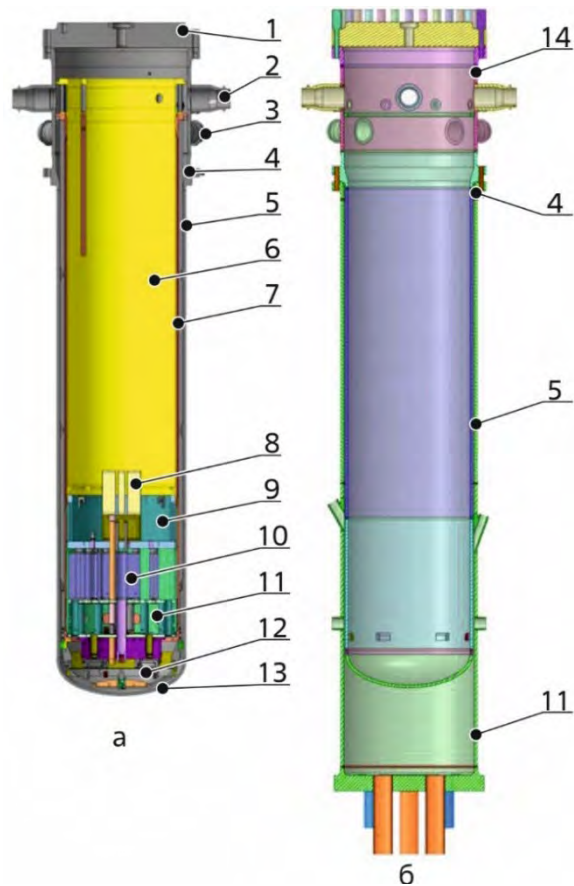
Общий вид реактора СМ (а), его корпуса и несущей конструкции (б): 1 — крышка корпуса; 2 и 3 — патрубки подвода и отвода теплоносителя соответственно; 4 — фланец соединения с несущей конструкцией; 5 — корпус; 6 — разделитель потока; 7 — экран; 8 — хранилище ТВС; 9 — прижимная решётка; 10 — блоки бериллиевого отражателя; 11 — несущие конструкции центральной зоны (нижняя и верхняя плита, гильзы, стаканы, корпус, обечайка); 12 — поддон; 13 — днище корпуса; 14 — коллектор
